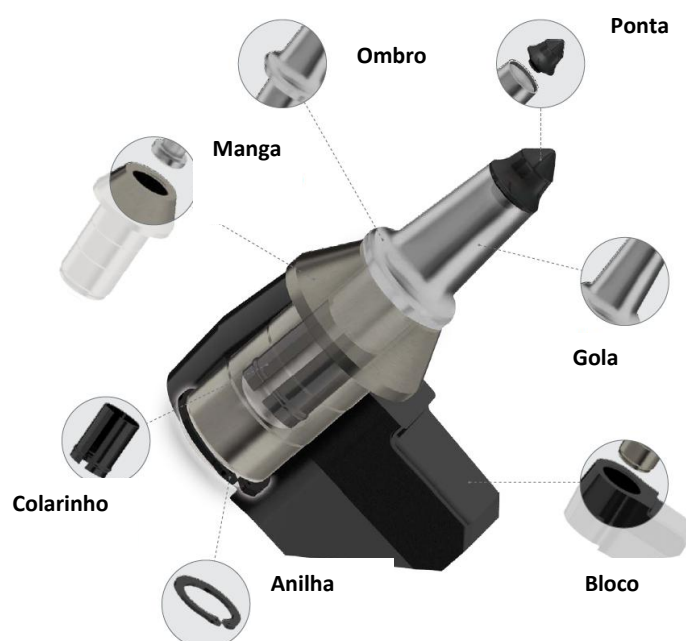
Constituição da ferramenta de corte (Sandvik, 2011)
